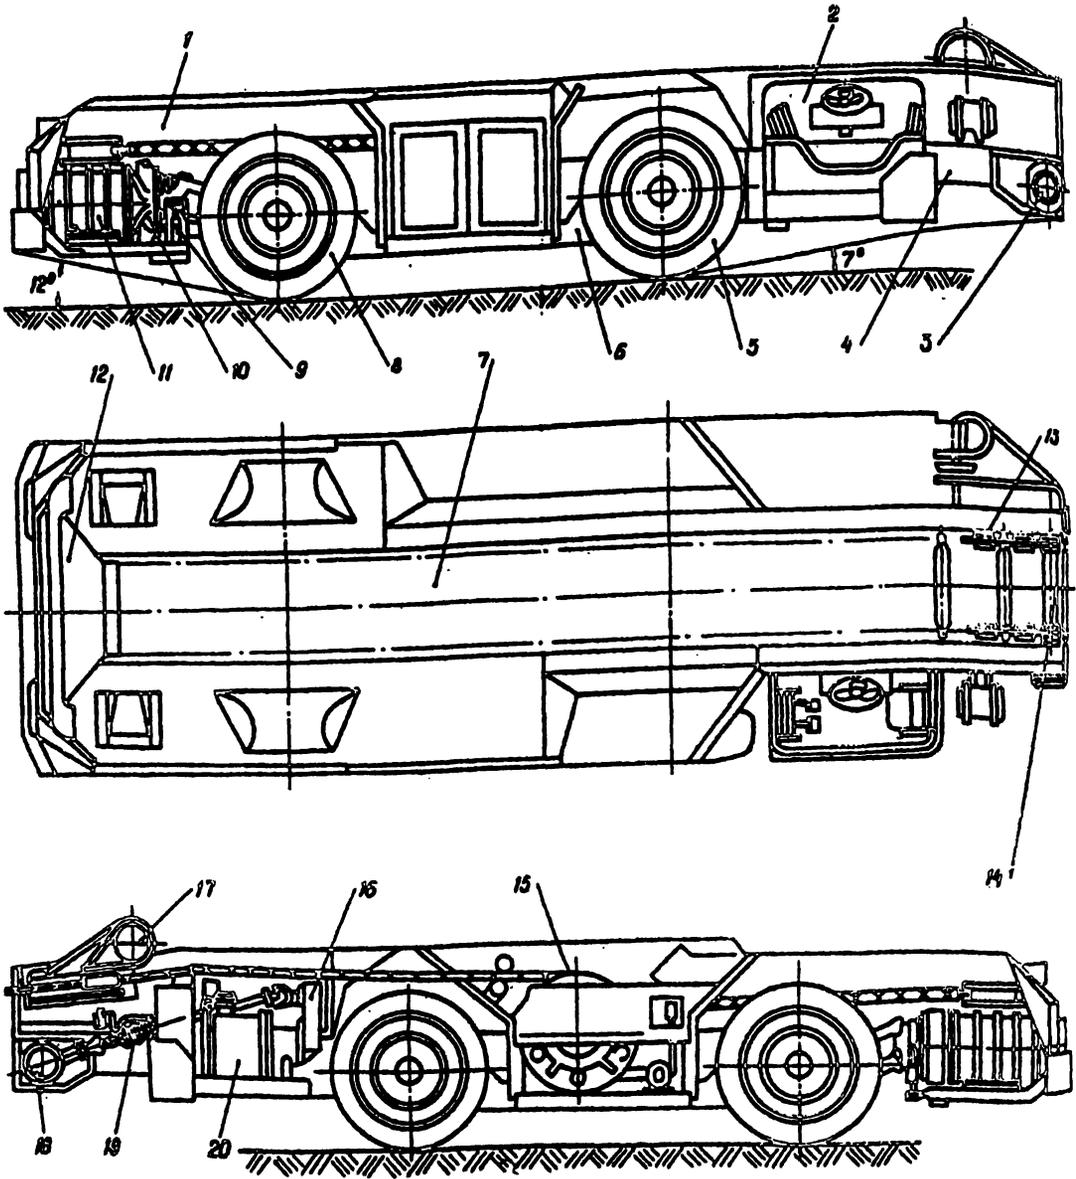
Общий вид шахтного самоходного вагона 5BC-15M
